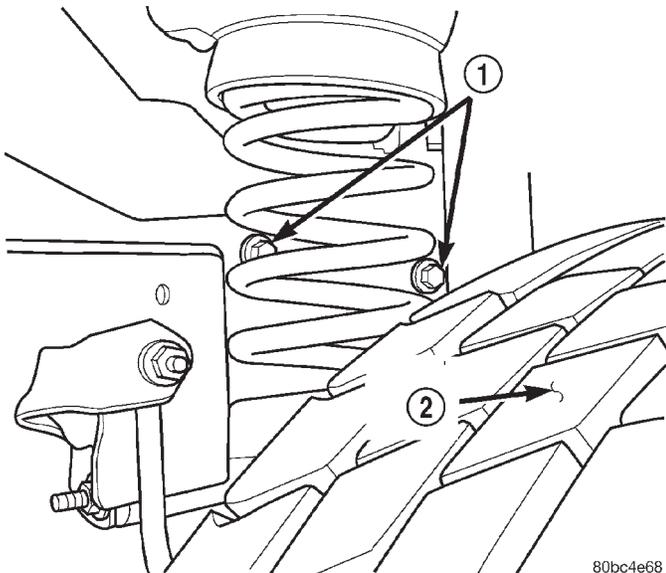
Schrauben des Sockels/Motoraufhängung—
